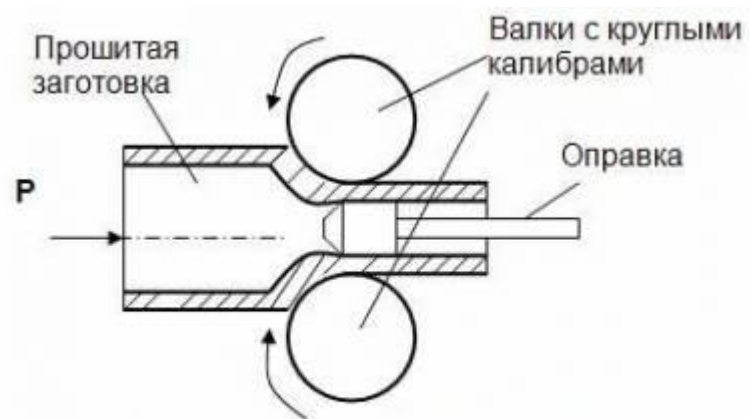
Схема прокатки прошитой заготовки на оправке
